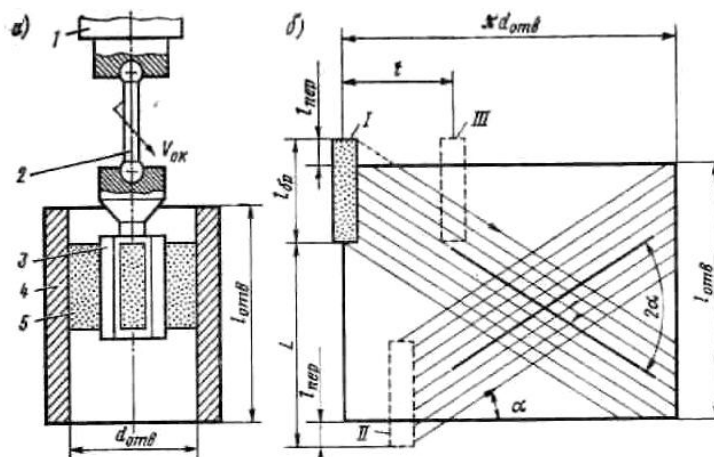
Схема процесу хонінгування (а) і розгортка сітки слідів обробки (б): 1 - шпіндель верстата; 2 - шарнірний пристрій; 3 - хонингувальна головка; 4 гільза; 5 - хонингувальний брусок; 2б - кут схрещування слідів; би - кут підйому сліду; I, II, III - послідовні положення бруска за один подвійний хід
